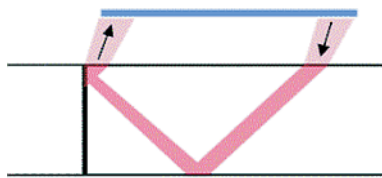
Arrays in Tandemtechnik zur Prüfung von Schweißnähten
